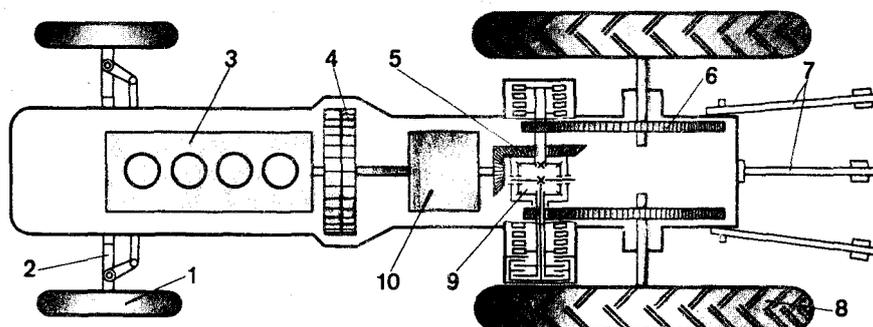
Расположение основных частей, их механизмов и деталей колесного трактора МТЗ-80:
